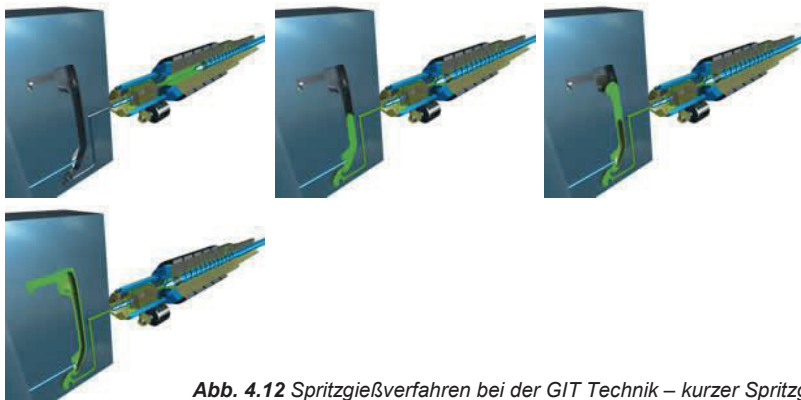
Spritzgießverfahren bei der GIT Technik – kurzer Spritzguss
